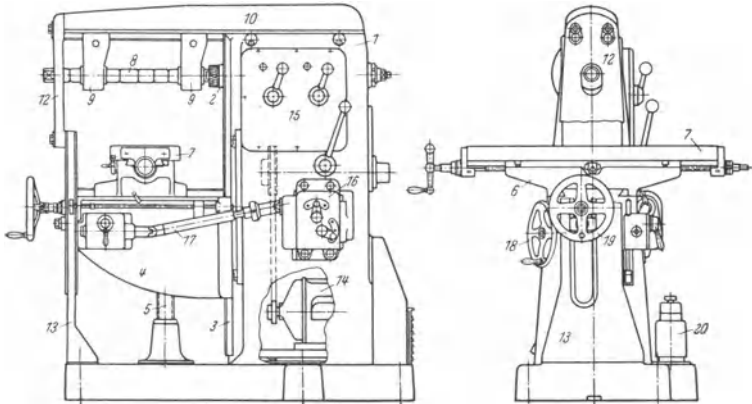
Einfach-Waagrechtfräsmaschine (Konsolfräsmaschine) (Fa. Krebs, Leipzig).
